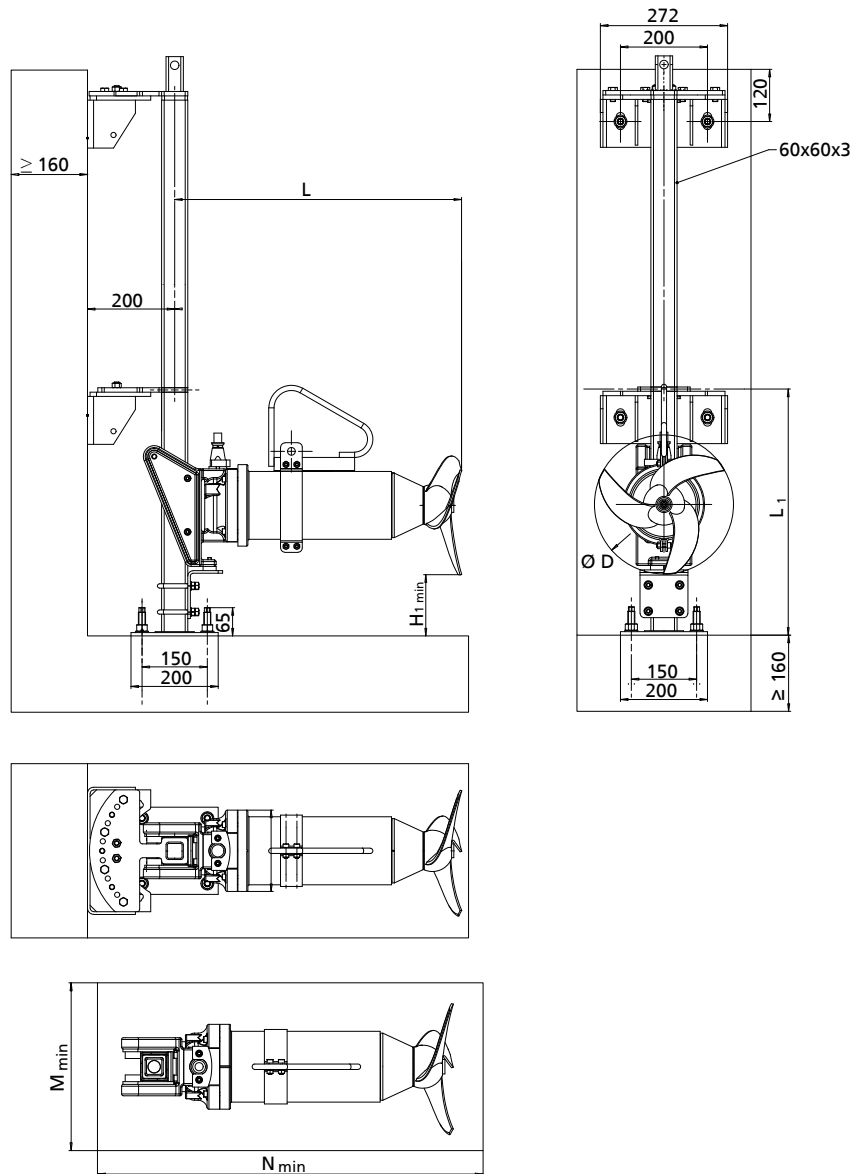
Установка принадлежностей 22 — Amamix 200/300/400 (внешний типоразмер 4135)
